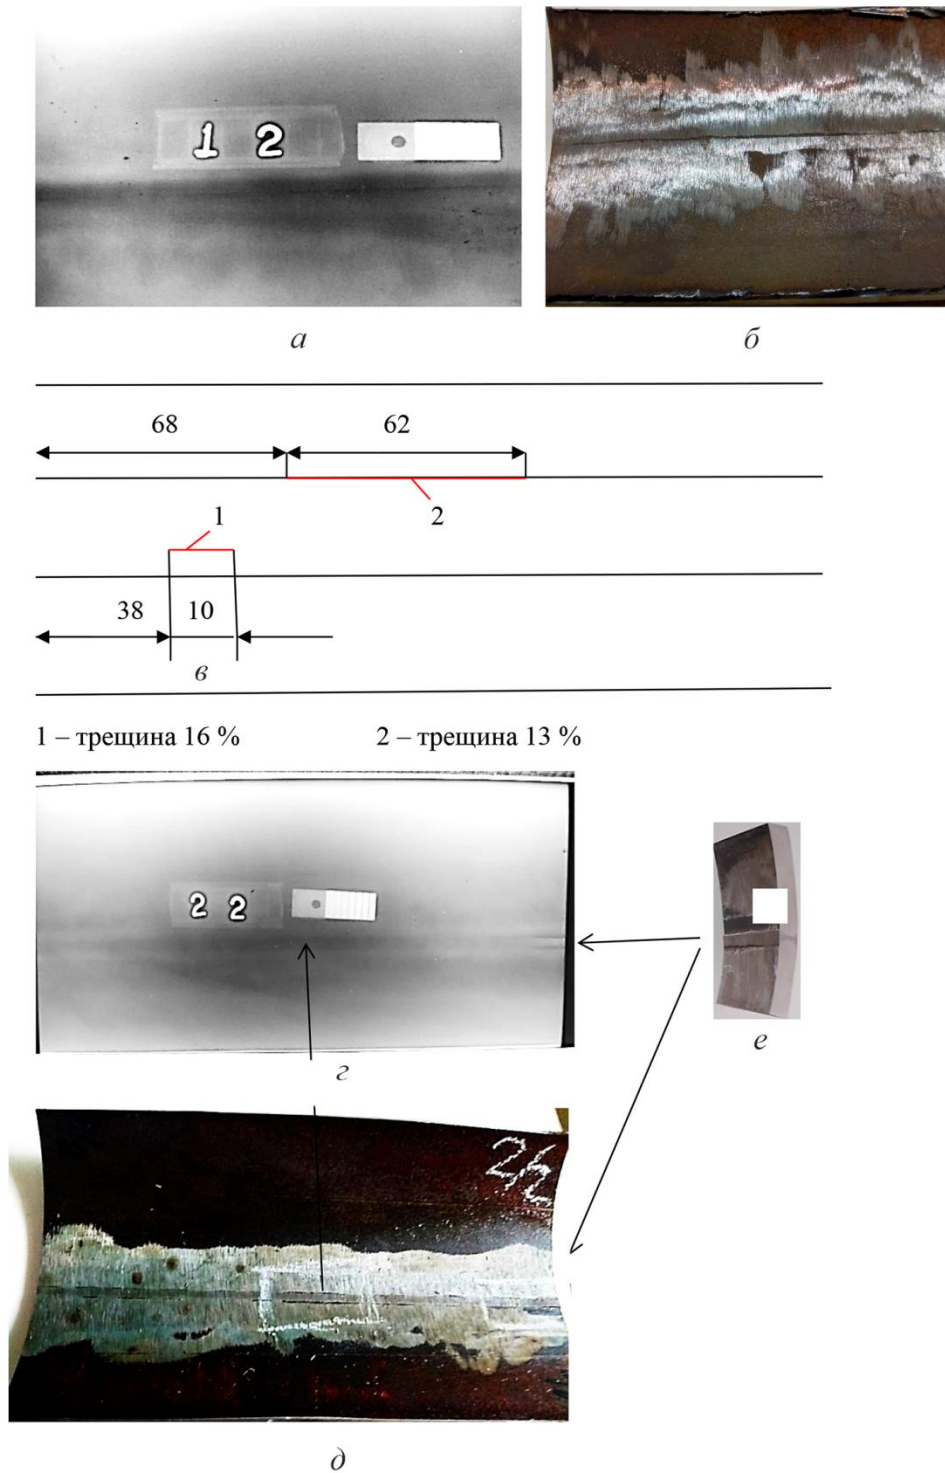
Корреляция рентгеновских снимков с околошовными дефектами на внутренней поверхности сварных соединений образцов труб: *а* – рентгеновский снимок зоны сварного соединения темплета из трубы 1.2; *б* – канавка на внутренней поверхности вдоль границы сварного соединения темплета трубы 1.2, коррелирующая с темной полосой на рентгенограмме; *в* – схема расположения трещины на внутренней поверхности сварного соединения темплета трубы 1.2; *г* – рентгеновский снимок зоны сварного соединения темплета из трубы 2.2; *д*, *е* – канавки на внутренней поверхности трубы вдоль границы сварного соединения темплета из трубы 2.2, коррелирующие с темными полосами на рентгенограмме
